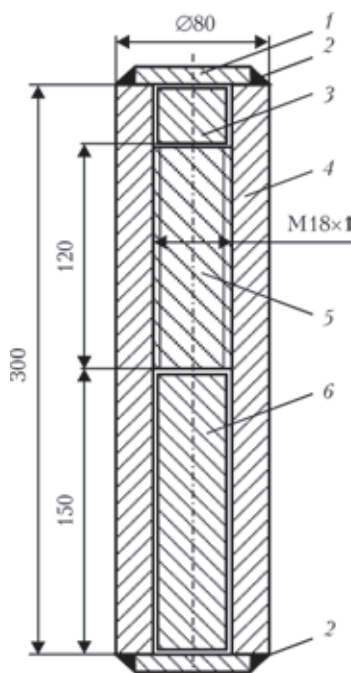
Схема образца для АВП в сборе: 1 — технологический фланец; 2 — герметизирующие швы; 3 — припой; 4 — корпус; 5 — стержень с резьбой; 6 — гладкий стержень
